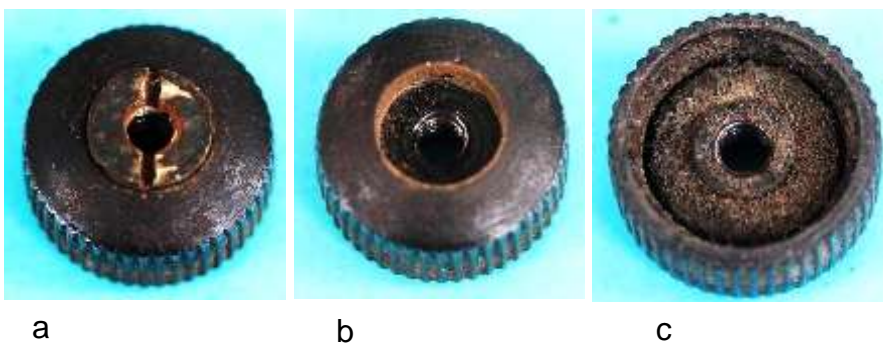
Reibrad: a) Reibrad mit Kontermutter, b) Gewindebohrung im Reibrad, c) Filzring im Innenraum
